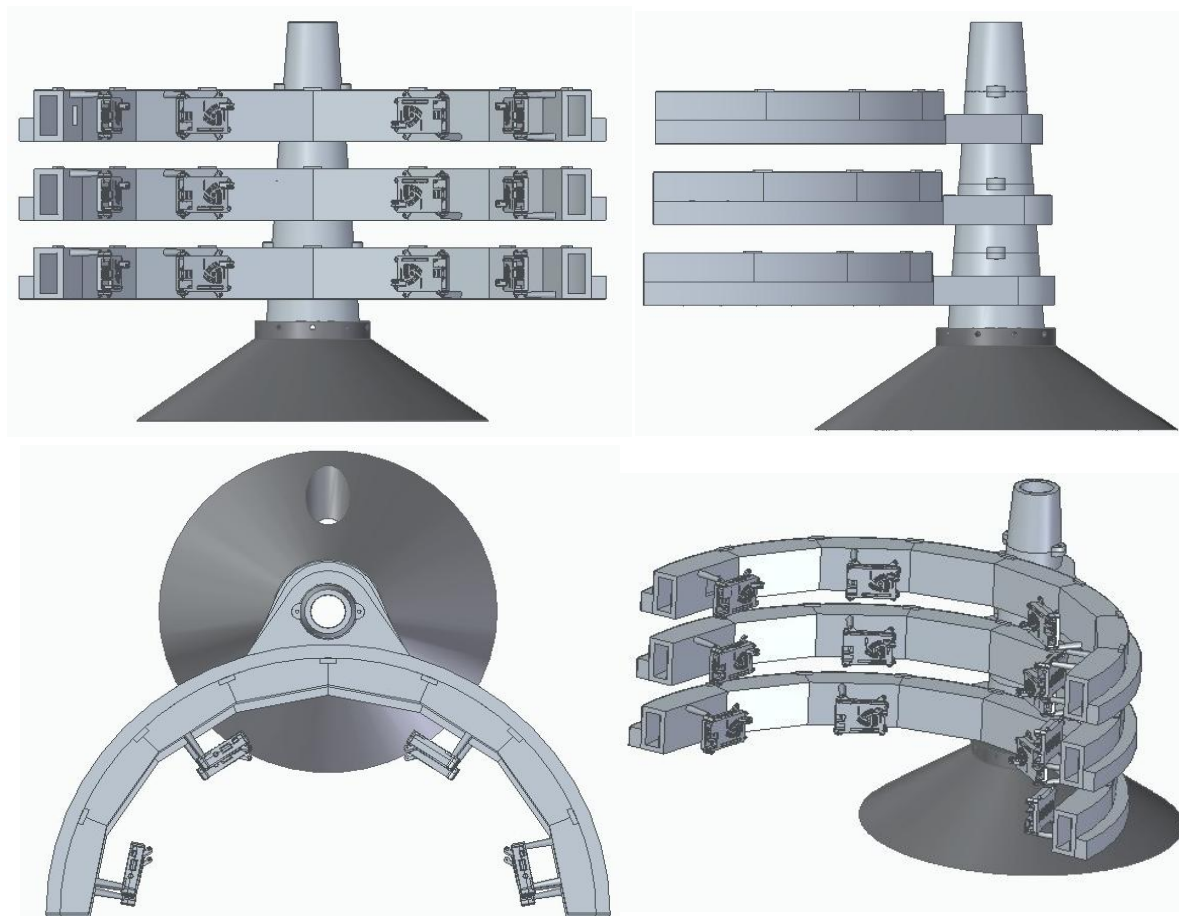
Alzado, planta, perfil y vista 3D de la tercera versión de la estructura.
